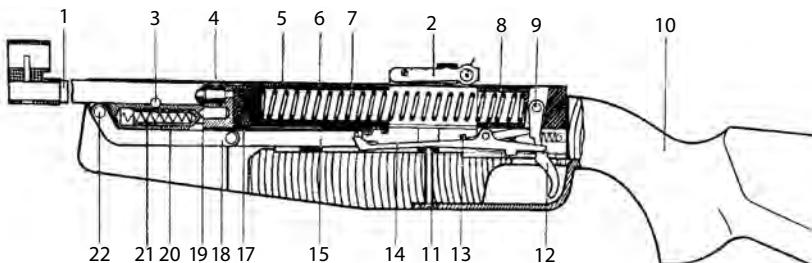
Пневматическая винтовка: 1 — ствол; 2 — прицел; 3 — ось ствола; 4 — прокладка ствола; 5 — ствольная коробка; 6 — поршень; 7 — боевая пружина; 8 — колодка спускового механизма; 9 — штифт колодки; 10 — ложа; 11 — задний винт ложи; 12 — спусковой крючок; 13 — шептало; 14 — рычаг блокировки; 15 — рычаг взвешивания; 17 — манжета; 18 — шарнир; 19 — клин; 20 — ригель; 21 — пружина ригеля; 22 — ось шарнира
